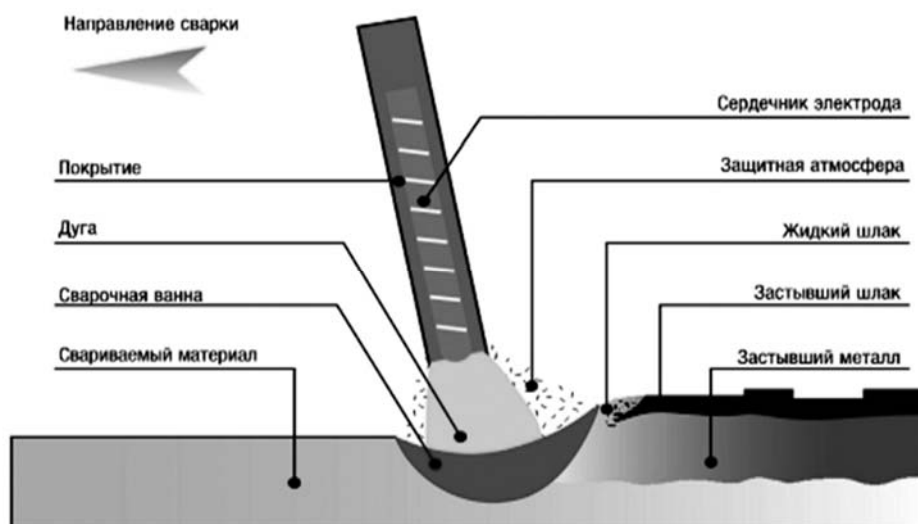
Схема ручной дуговой сварки
